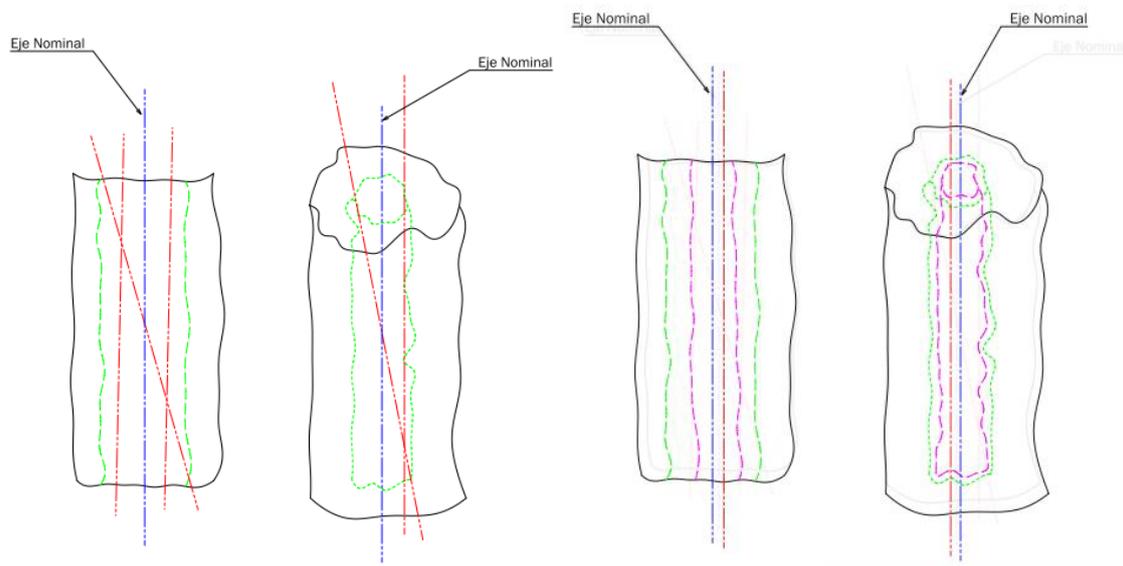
Representación de especificación de posicionamiento (izquierda) y perpendicularidad (derecha) en la interfaz pump housing-engine
